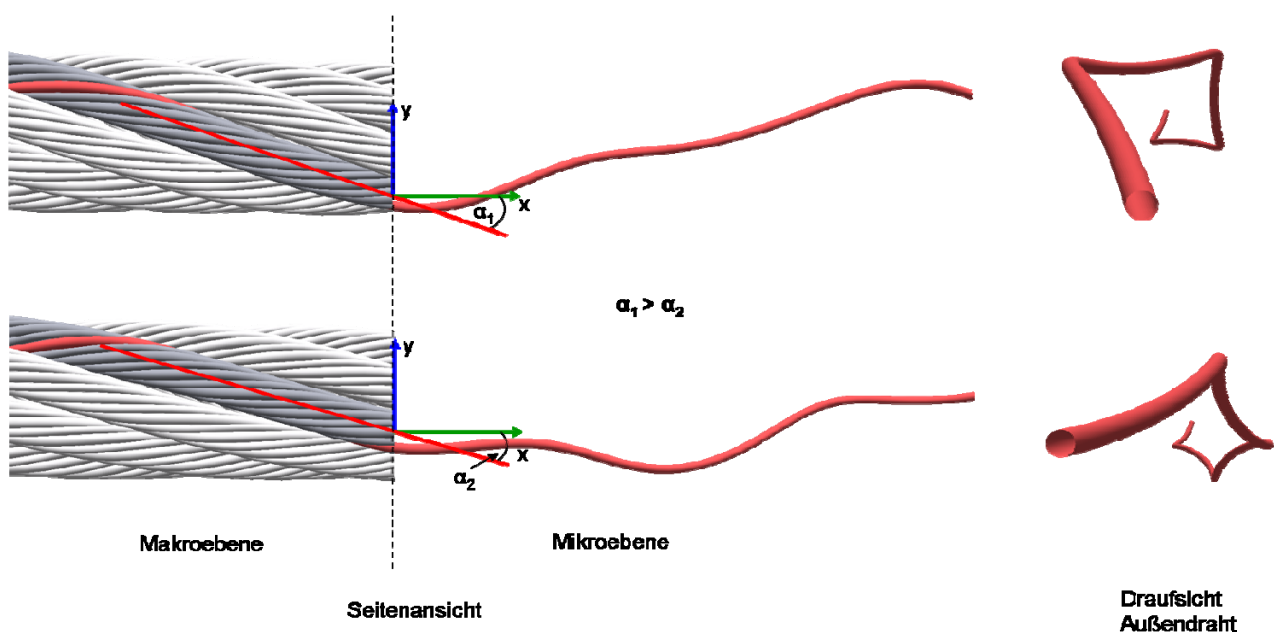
Geometrieänderungen im Seil durch Verdrehung
